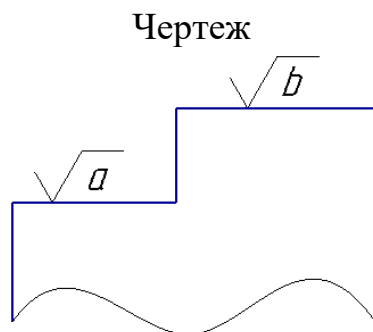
Пример обозначения шероховатости на чертеже
